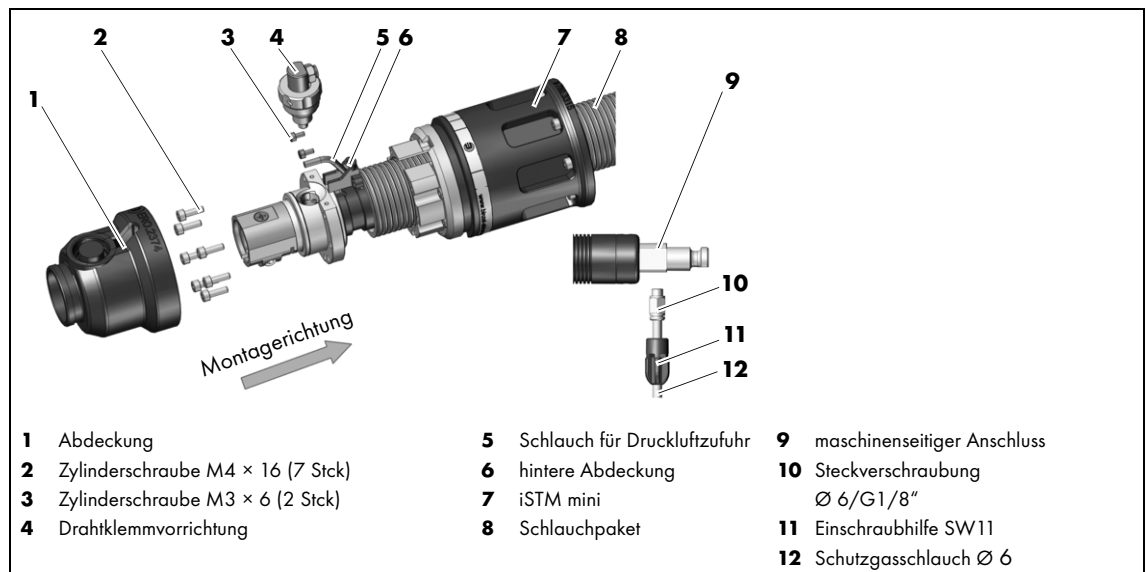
Schlauchpaket montieren iSTM mini für ABIROB® G mit Wire-Brake
